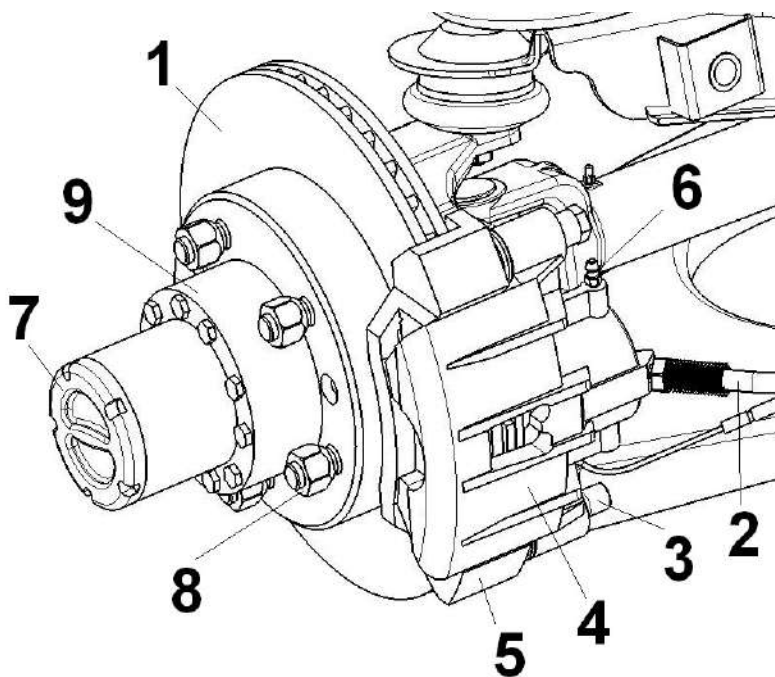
Тормозной механизм переднего колеса: 1- тормозной диск; 2- тормозной шланг; 3- болт; 4- суппорт; 5- направляющая колодок; 6- штуцер прокачки; 7- поворотный маховик включения привода; 8- гайка крепления колеса; 9- ступица
